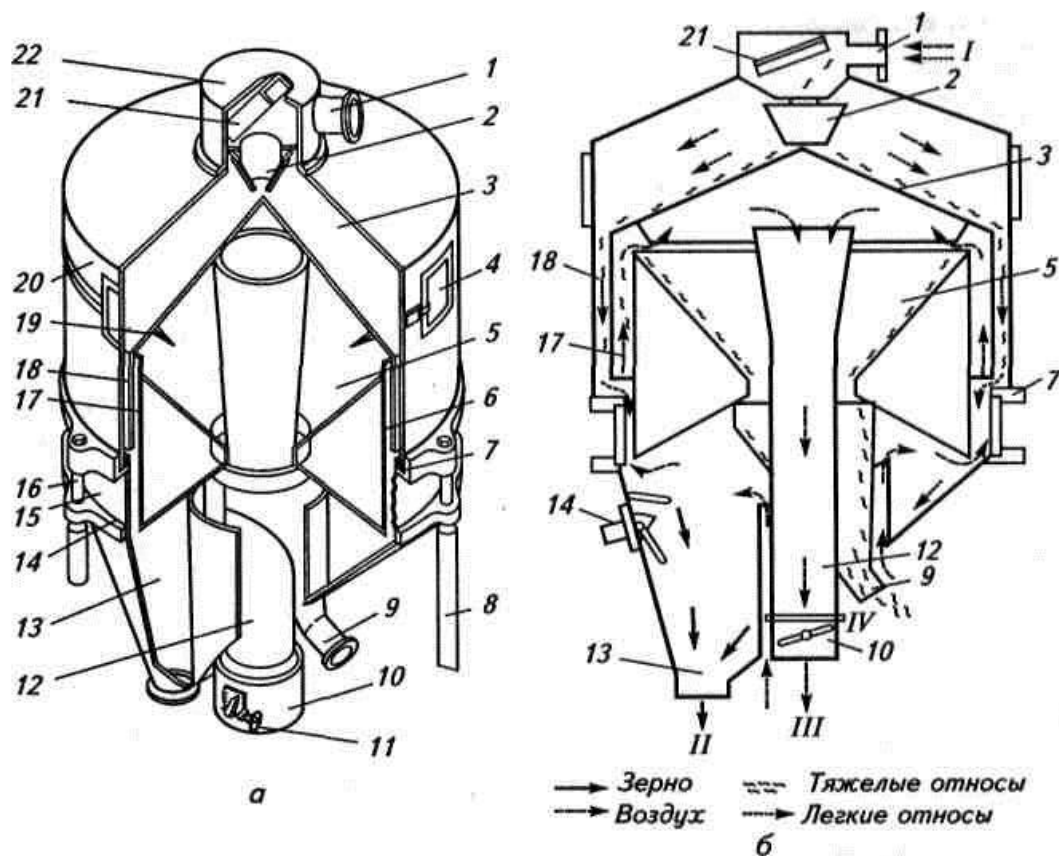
Пневматический сепаратор РЗ-БСД: *а* — конструкция; *б* — технологическая схема; 1— приемный патрубок; 2— направляющая воронка; 3— распределительный конус; 4, 15— смотровые окна; 5— осадочная камера; 6— внутренний кожух; 7— направляющее кольцо; 8— опора; 9— патрубок для тяжелых отноров; 10— дроссельная насадка; 11 — регулятор дроссельной заслонки; 12— отсасывающий патрубок; 13— выпускной патрубок для очищенного зерна; 14— электросигнализатор; 16— стойка; 17— пневмосепарирующий канал; 18— внешний канал; 19— козырек; 20— корпус; 21 — отражатель; 22— приемное устройство; I - зерно с воздухом; II - очищенное зерно; III - воздух с легкими отнорсами; IV— тяжелые отнорсы
